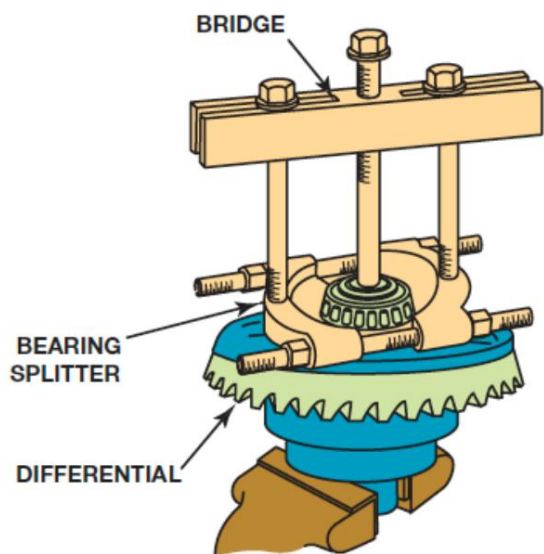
Se instala un extractor y un divisor de cojinetes para quitar el cojinete lateral del diferencial.
